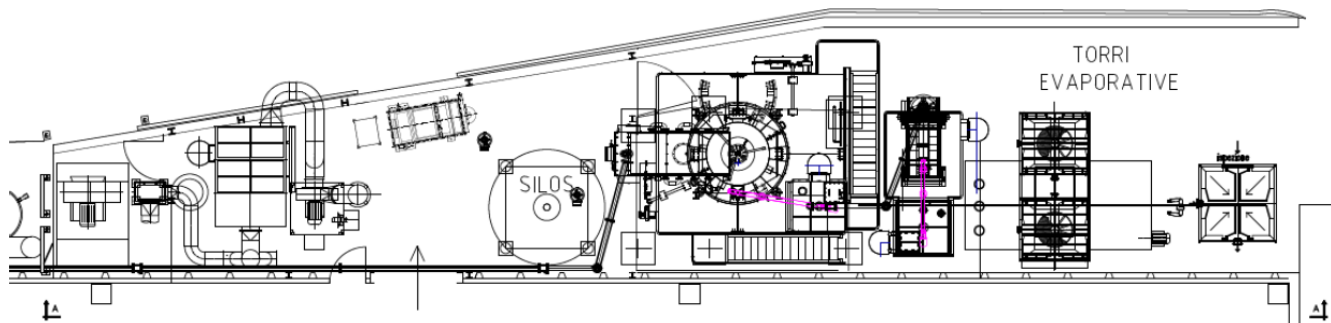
Layout nuovo impianto rigenerazione sabbia
